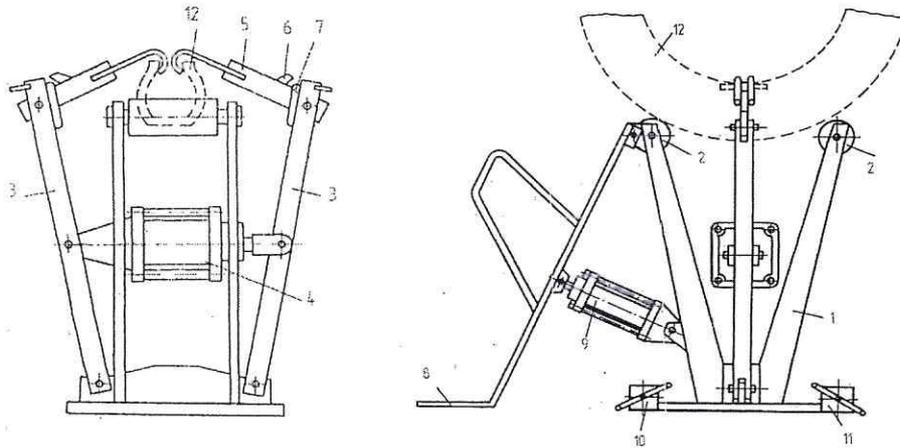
Устройство для осмотра и ремонта покрышек
